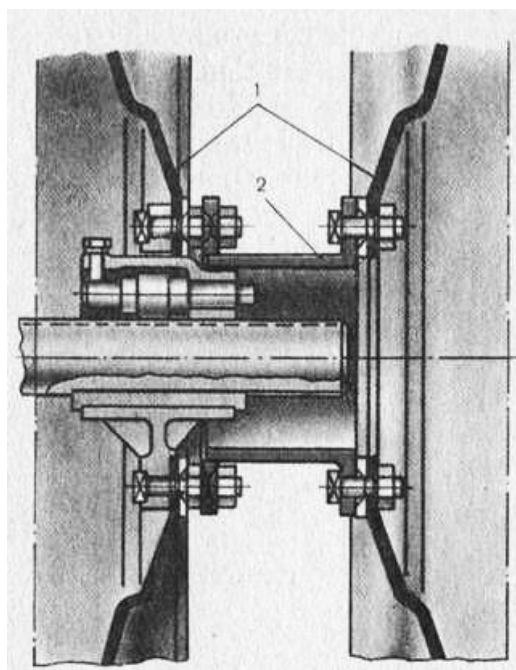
Установка сдвоенных ведущих колес трактора МТЗ-80: 1 — диски; 2 — проставка.
